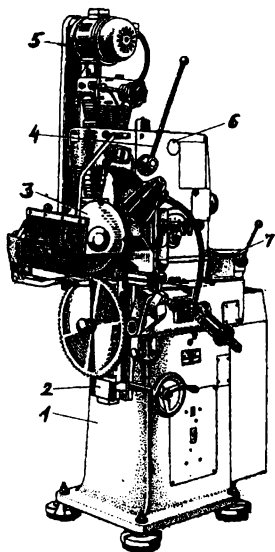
Универсальный пилоточный станок ТчПА-5
